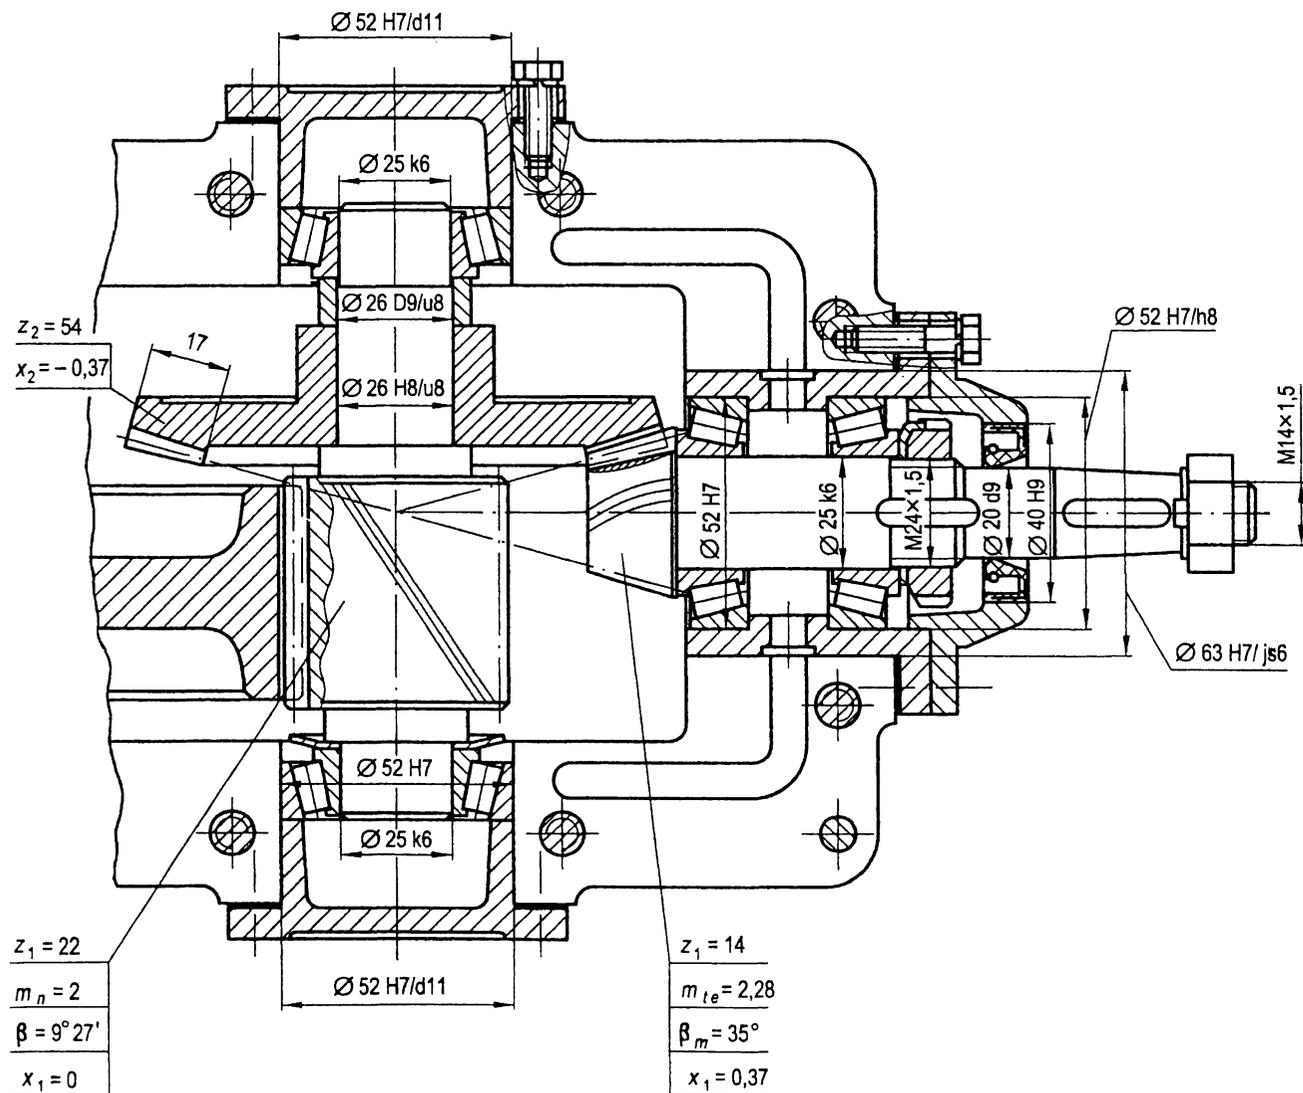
Быстроходный и промежуточные валы коническо-цилиндрического горизонтального редуктора, выполненного с разъемом корпуса по осям валов
